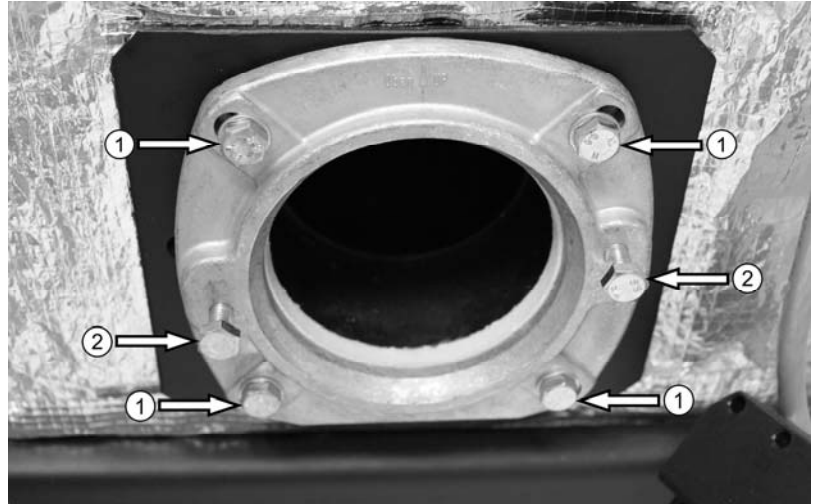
Kesselflansch mit den vier Schrauben ① an Kesseltür befestigen. Die zwei Brennerbefestigungsschrauben ② mit ca. fünf Umdrehungen in die Kesseltür einsetzen.
